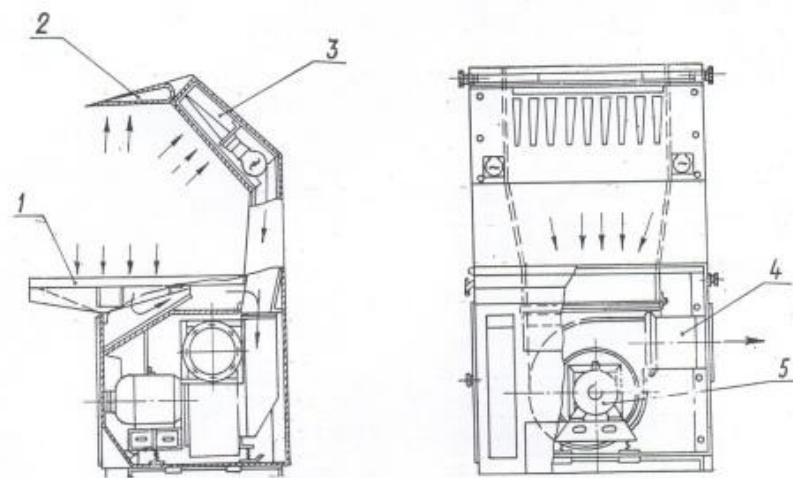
Стіл зварника з вмонтованою вентиляцією (УкрІЗВ): 1 – нижня всмоктувальна решітка; 2 – поворотний козирок; 3 – нахилена панель рівномірного всмоктування; 4 – патрубок; 5 – вентиляційний агрегат [65]
